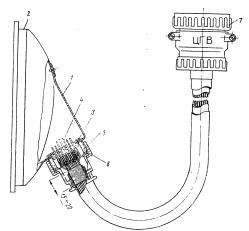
Кожух прибора с кольцом. 1-кожух прибора, 2-кольцо крепления к корпусу.
